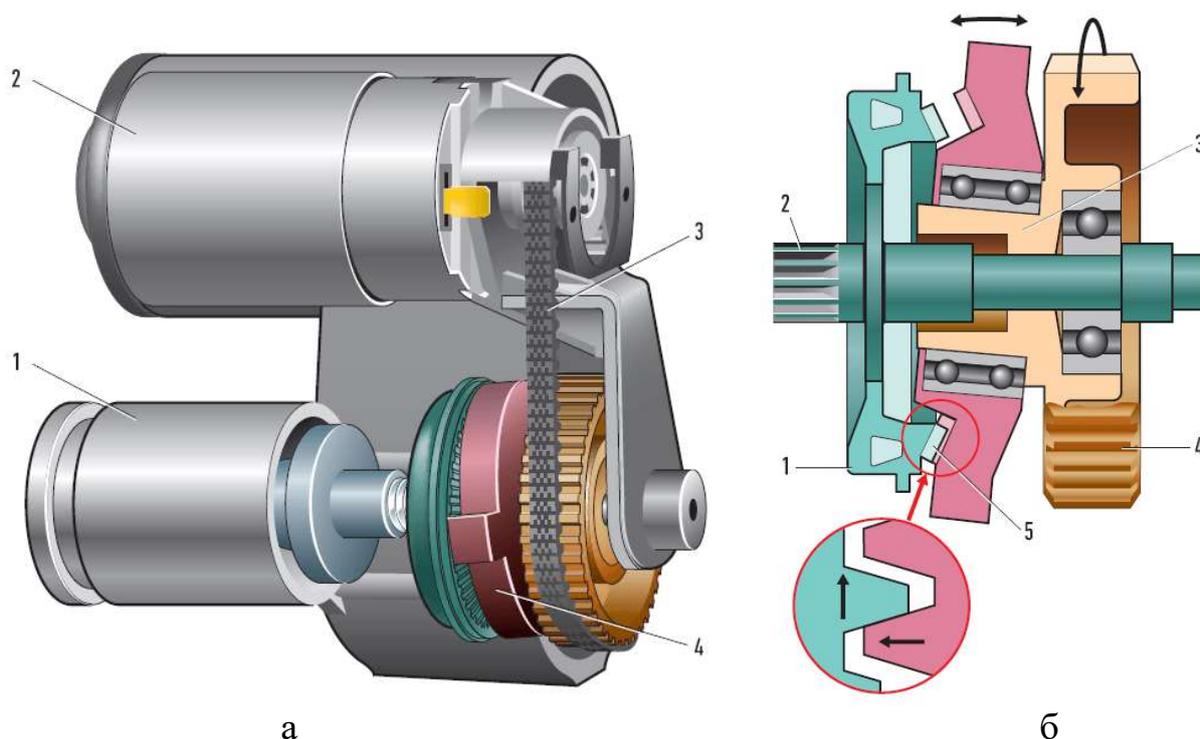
Привод стояночного тормоза с винтовой передачей:
